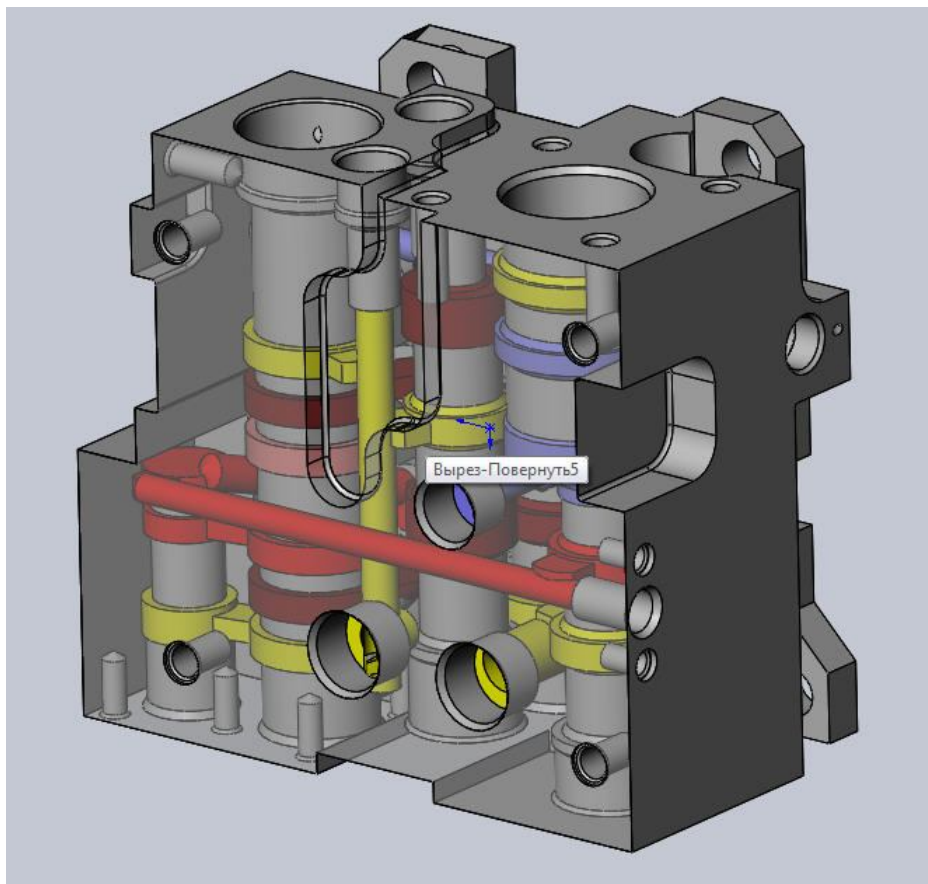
Твёрдотельная модель корпуса агрегата двигателя
